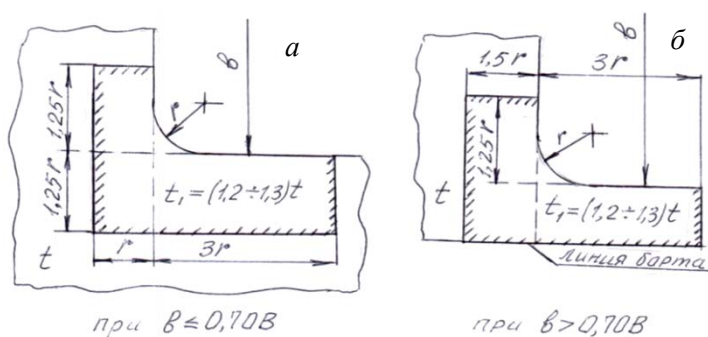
Подкрепление углов прямоугольных вырезов в палубах сварными утолщенными листами:
